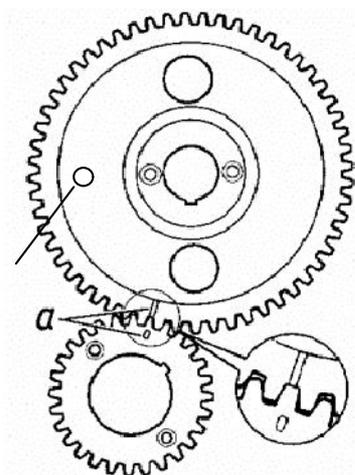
Установочные метки на шестернях распределительного и коленчатого валов
